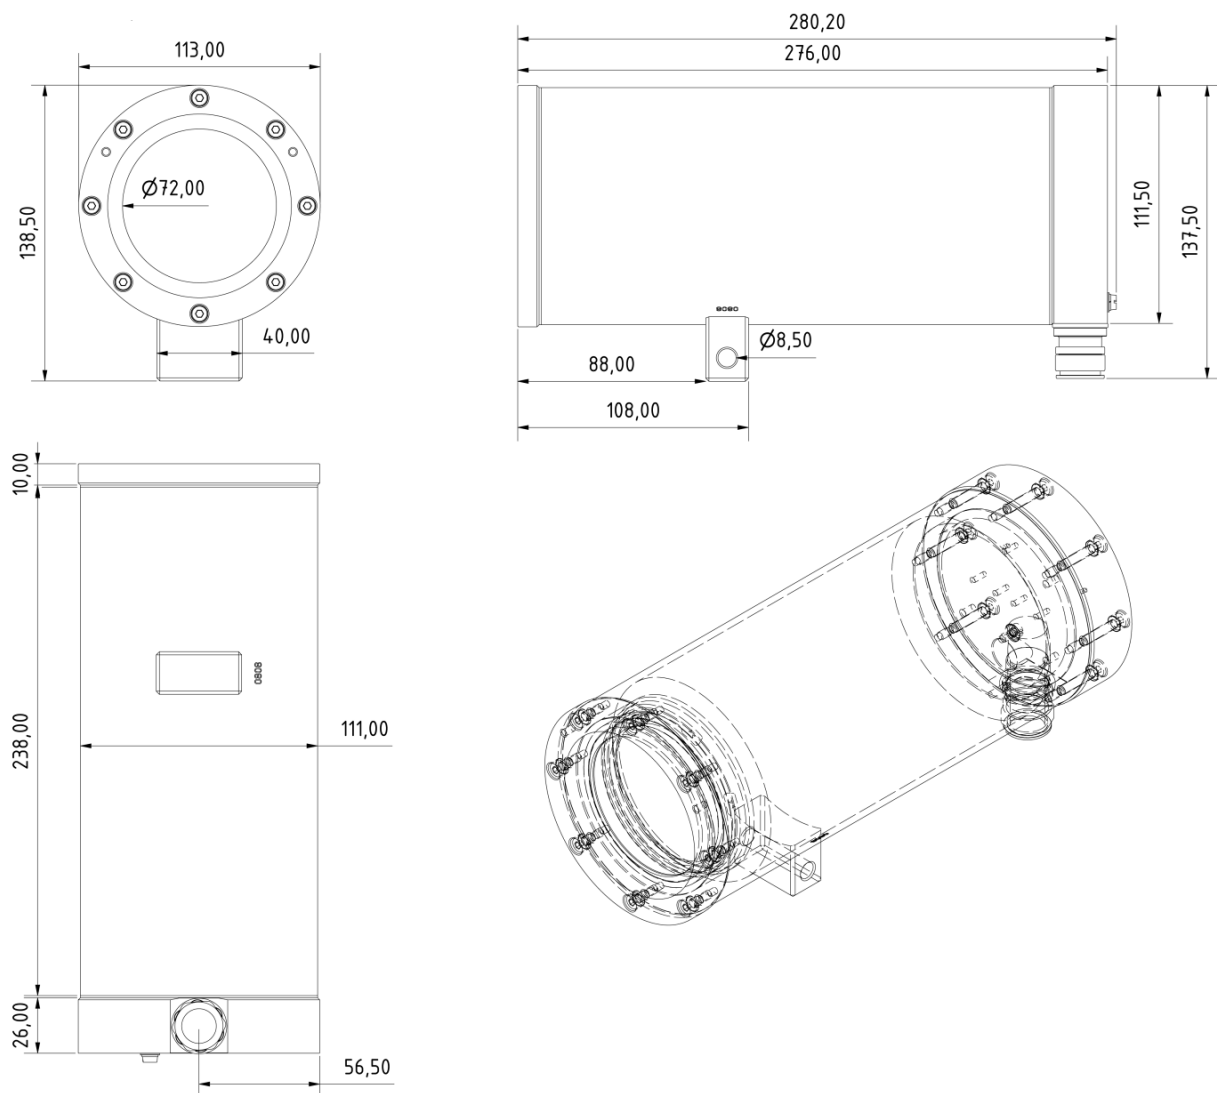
Abmessungen T08 ExCam IPQ1755 mit K2 Flansch
